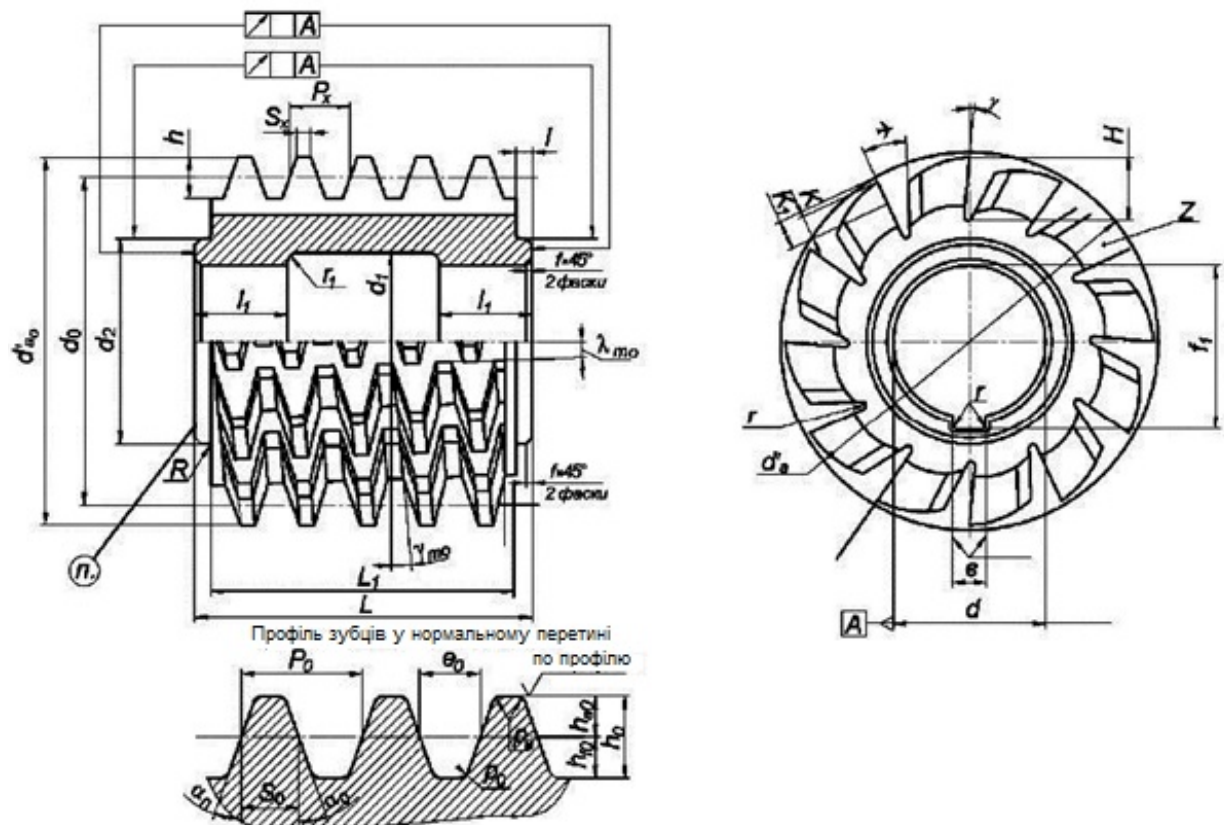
Черв'ячна фреза для нарізування циліндричних зубчастих коліс
